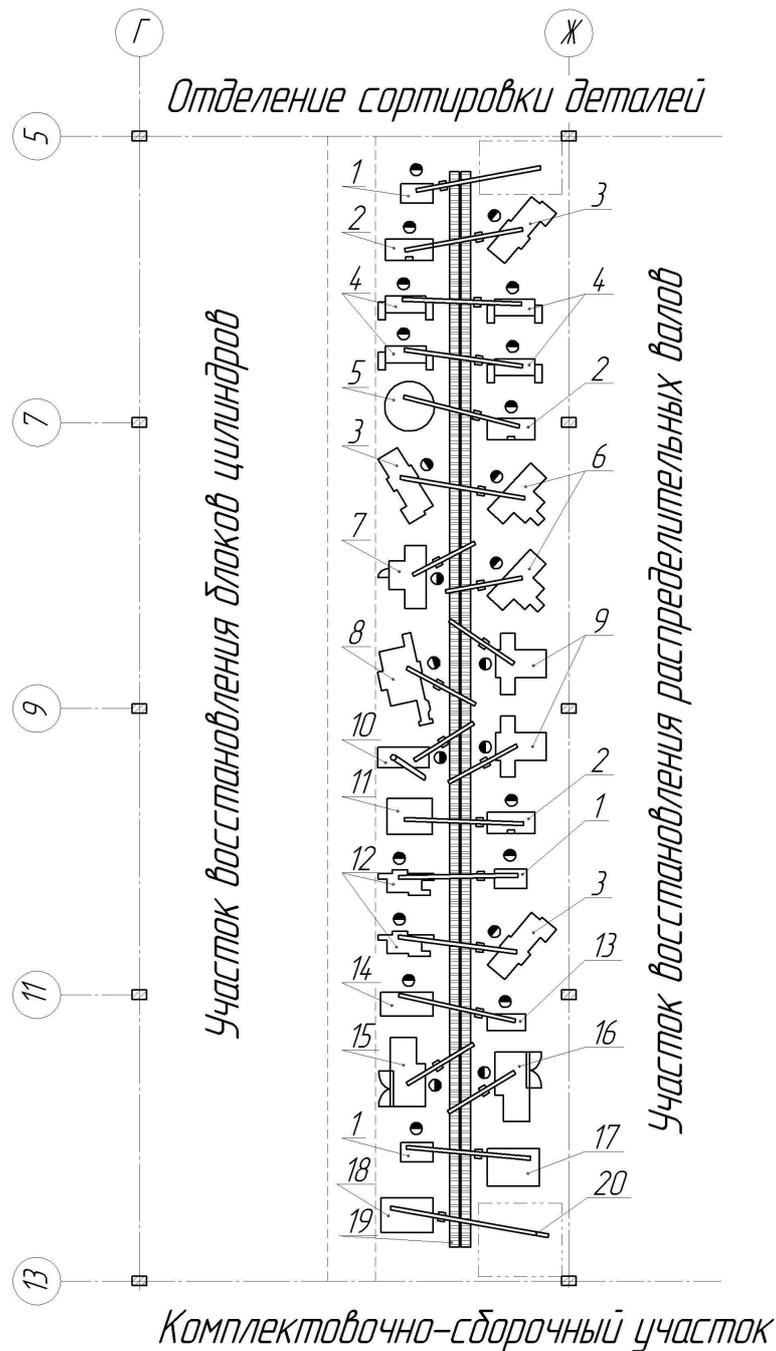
Схема планировки участка восстановления коленчатых валов двигателей КамАЗ-53212: 1 – магнитный дефектоскоп МД-50П; 2 – пресс гидравлический П-6326; 3 – станок токарно-винторезный 16К20; 4 – станок наплавочный У-653М; 5 – печь электрическая шахтная СШО-10.10/10М1; 6 – станок круглошлифовальный 3М152; 7 – станок круглошлифовальный 3В423; 8 – полуавтомат торцешлифовальный 3342А; 9 – станок горизонтально-фрезерный 6Р83Г; 10 – станок радиально-сверлильный 2К52; 11 – стенд для закалки ТВЧ шеек (обслуживается высокочастотным генератором ВЧГ-100/0,66 УЧ); 12 – полуавтомат круглошлифовальный ХШ2-12Н; 13 – стенд сборочный 70-7362-1518; 14 – станок балансировочный МС-9716; 15 – полуавтомат суперфинишный 3875К; 16 – полуавтомат полировальный 3835К; 17 – установка для очистки ОМ-3600; 18 – ванна для роликовой 12398; 20 – склиз
